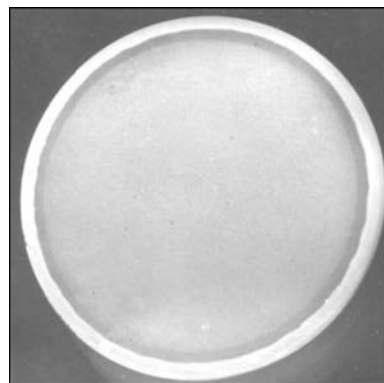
Макрошлиф поперечного сечения цилиндрической части штока задвижки DN 50, наплавленного плазменно-порошковым способом
